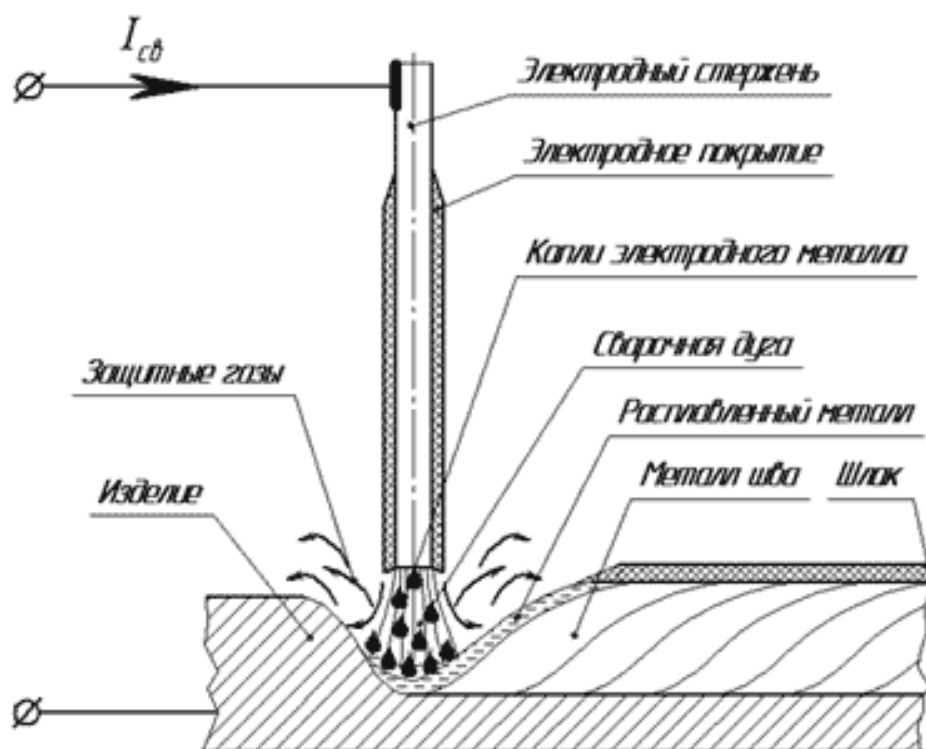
Схема сварки ручной дуговой сварки штучным электродом
